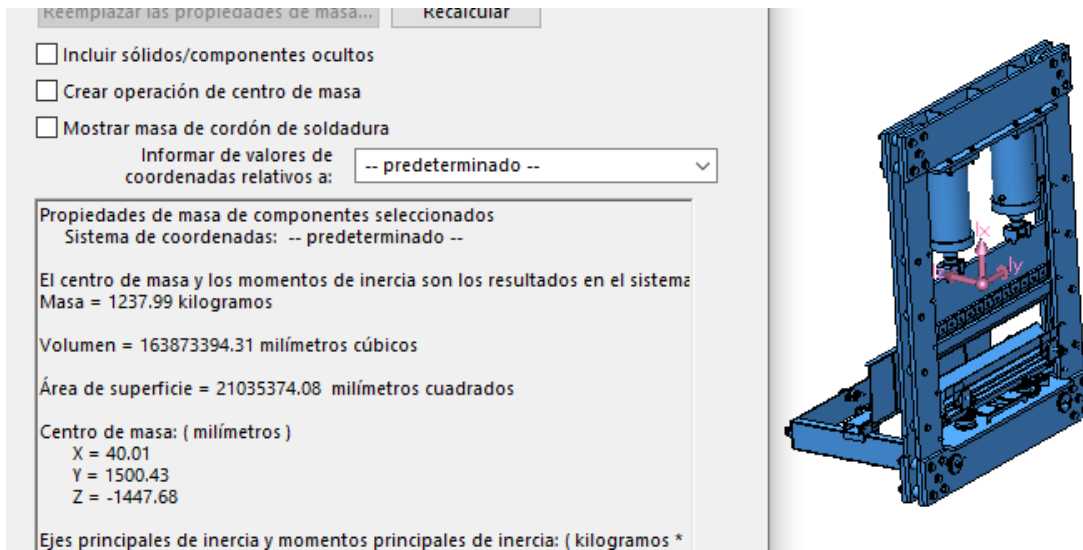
Propiedades físicas del conjunto de mecanismos de la máquina plegadora.
